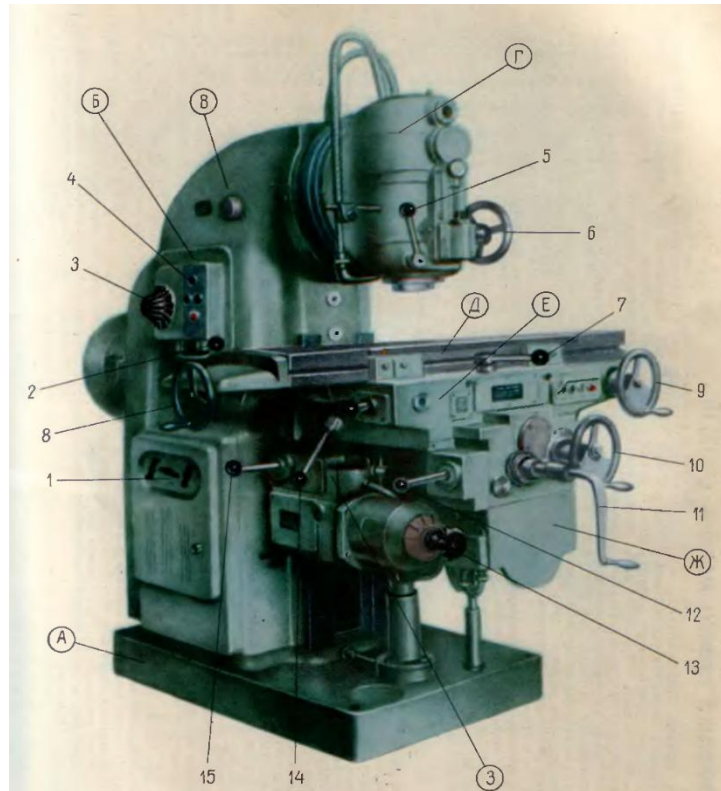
Вертикально-фрезерний верстат моделі 6Н12ПБ [9].
